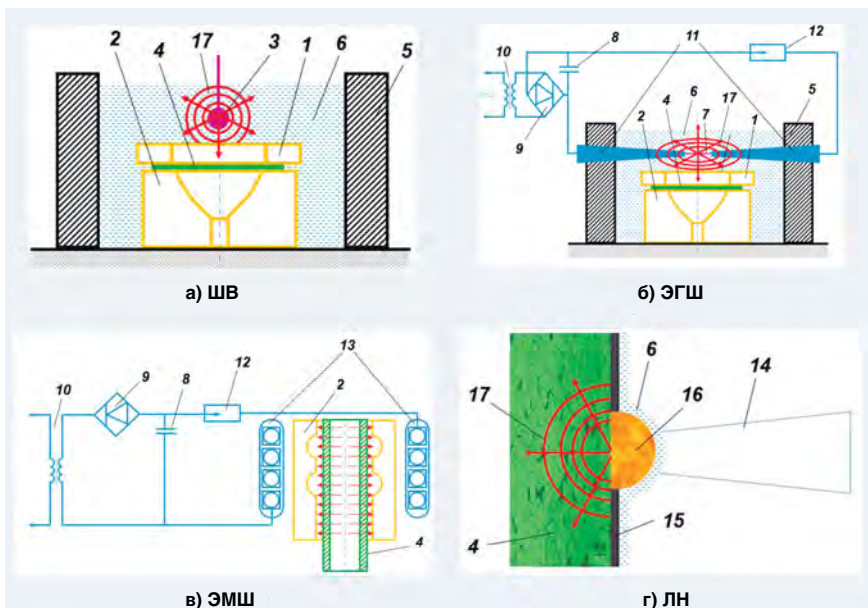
Схемы импульсных процессов: 1 — прижимное кольцо; 2 — матрица; 3 — заряд ВВ; 4 — заготовка; 5 — стенка контейнера; 6 — жидкая передающая среда; 7 — нить накаливания; 8 — конденсатор; 9 — выпрямитель; 10 — трансформатор; 11 — электроды; 12 — разрядник; 13 — индуктор; 14 — лазерное излучение; 15 — плёнка ПВХ; 16 — плазма; 17 — ударная волна
